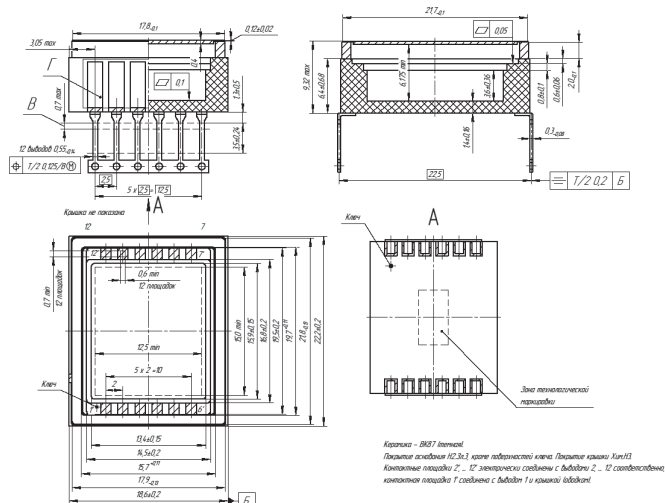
Габаритные, установочные и присоединительные размеры корпуса МК 2154.12-1
